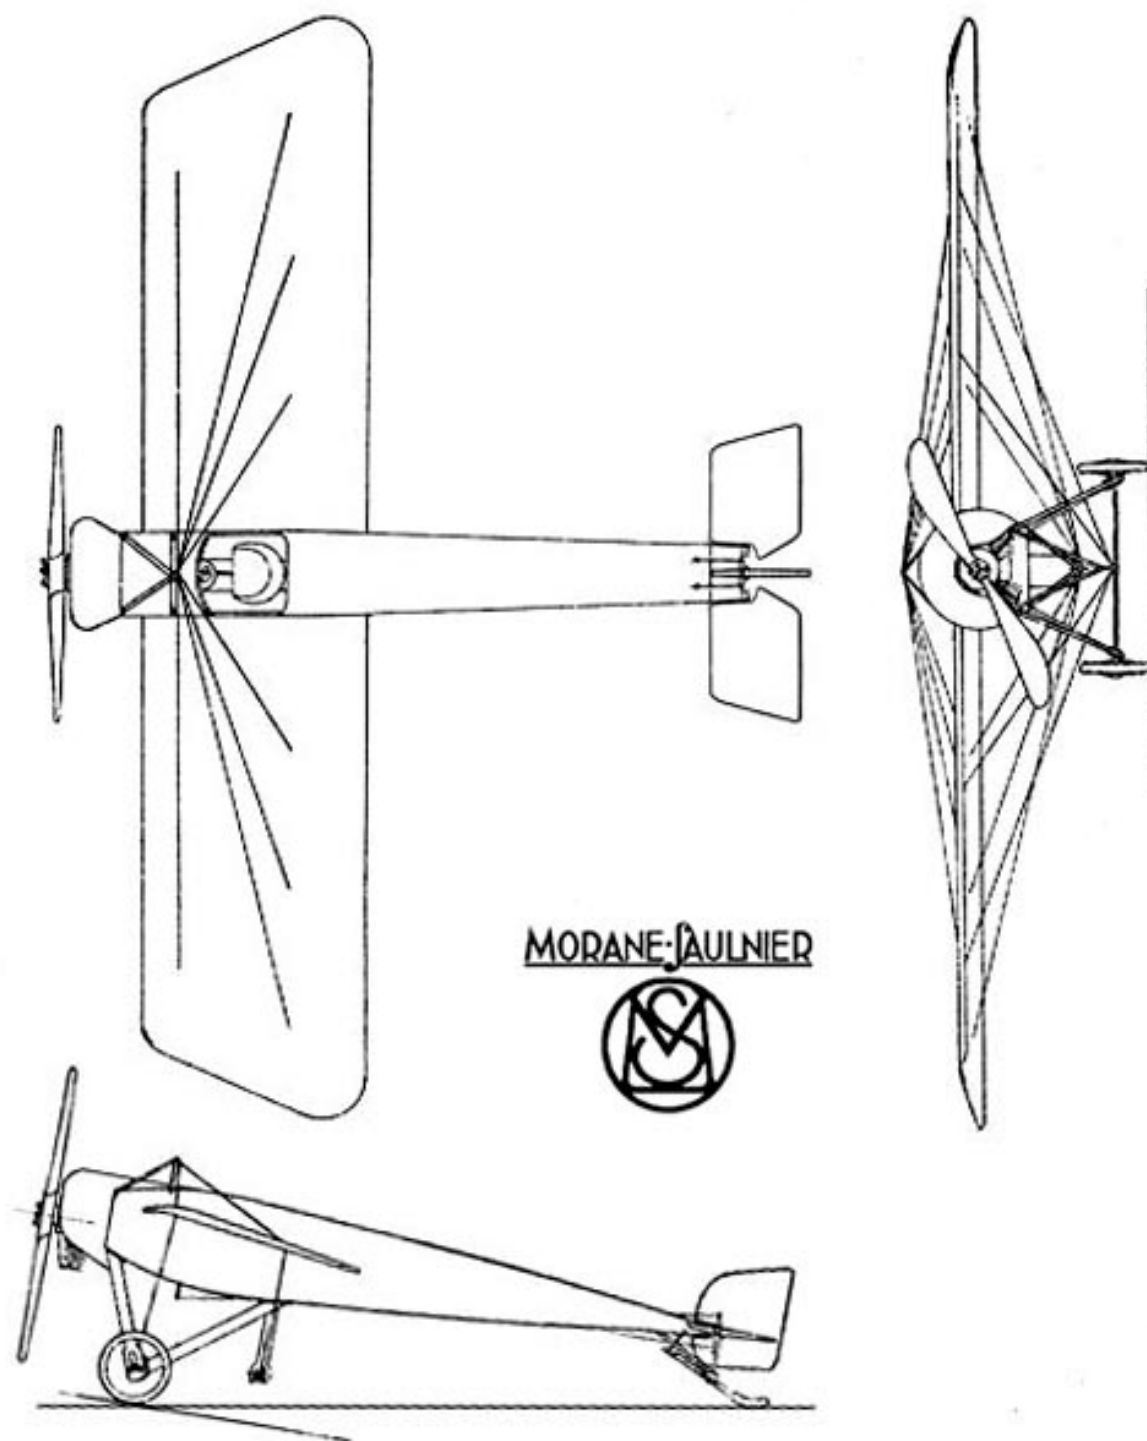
Planta da aeronave Morane-Saulnier tipo H ,
